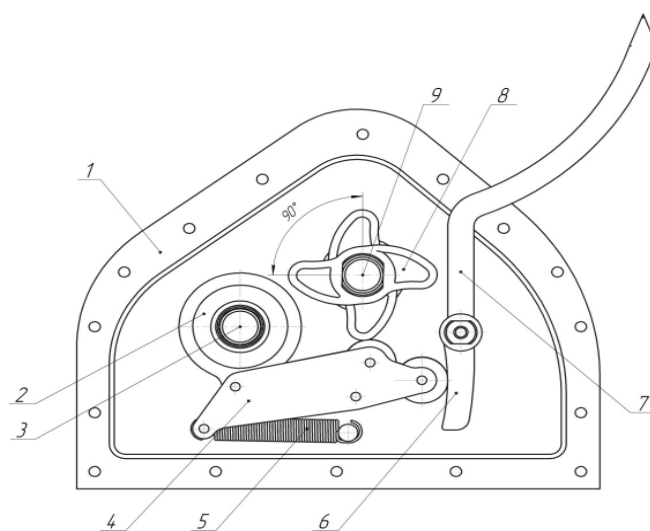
Конструкция бесступенчатого редуктора-вариатора: 1 – корпус; 2 – обгонные муфты; 3 – ведомый вал; 4 – рычаги толкателей; 5 – пружины; 6 – регулировочный рычаг; 8 – кулачки; 9 – ведущий вал
